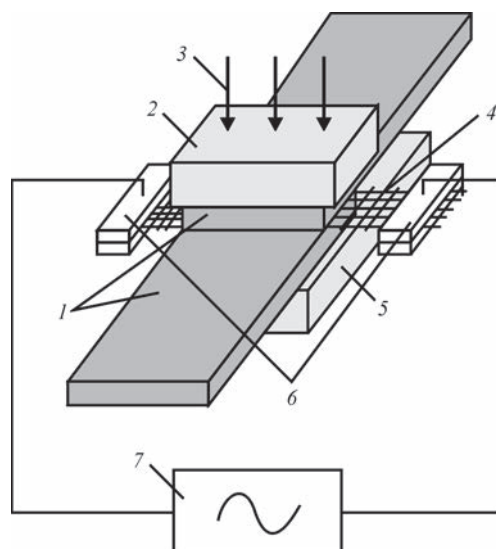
Схема процесса сварки закладным элементом: 1 — образцы; 2 — прижим; 3 — рабочее давление; 4 — закладной элемент; 5 — основание; 6 — электроконтакты; 7 — источник питания
